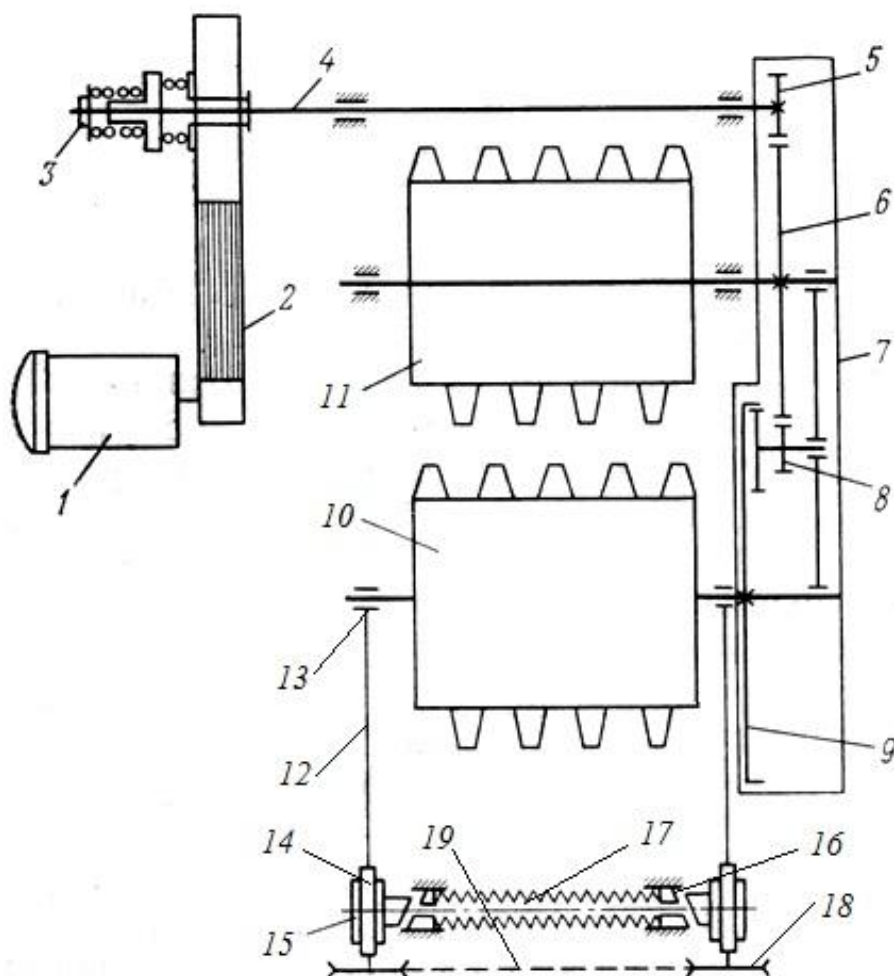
Кинематическая схема дробилки двухвалковой зубчатой ДДЗ:
